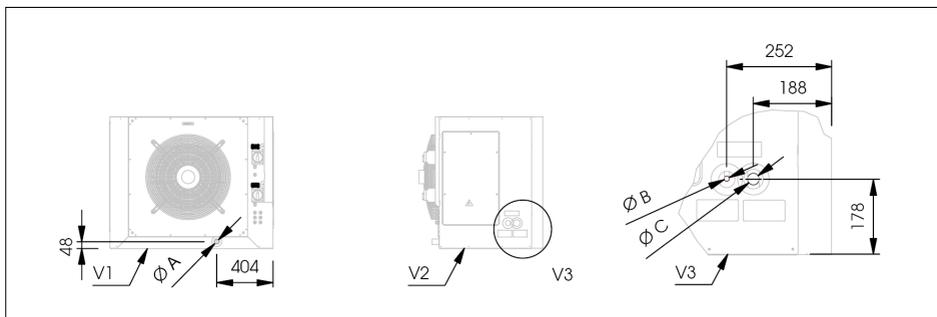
Dimensions des connexions MISTRAL MDX 30. (V1 : Vue arrière, V2 : Vue latérale gauche)
